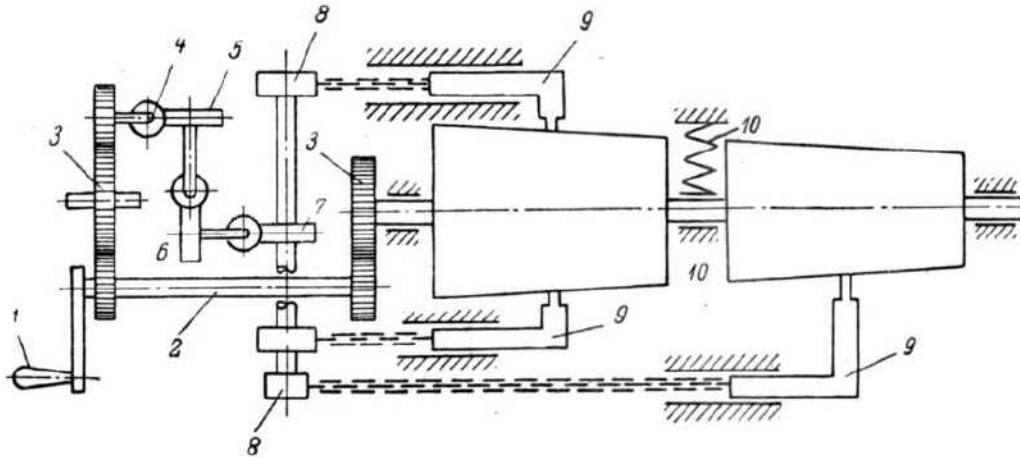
Кинематическая схема токарно-копировального станка для фасонной обточки продолговатых деталей с выпуклыми орнаментами на боковой поверхности (по И. А. Дружинскому):
